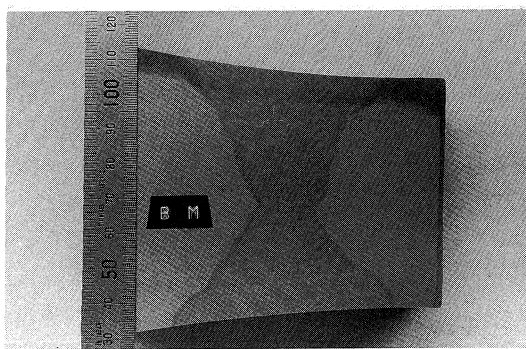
極厚板の板継ぎ溶接部のマクロ写真
